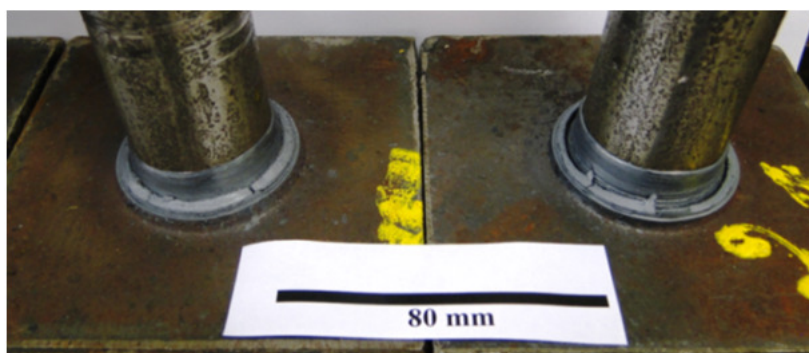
Solda no corpo de prova G03CP20 e G03CP21.
